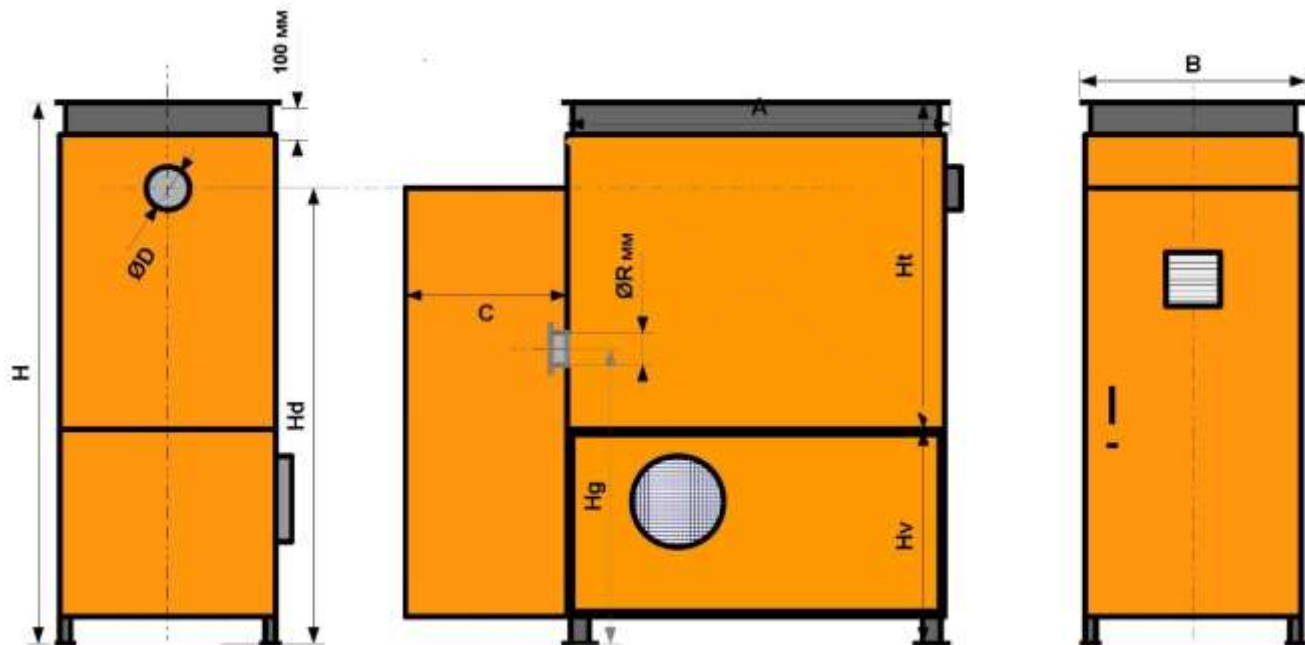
Габаритные размеры воздухонагревателей (теплообменников) серии VT-PT
